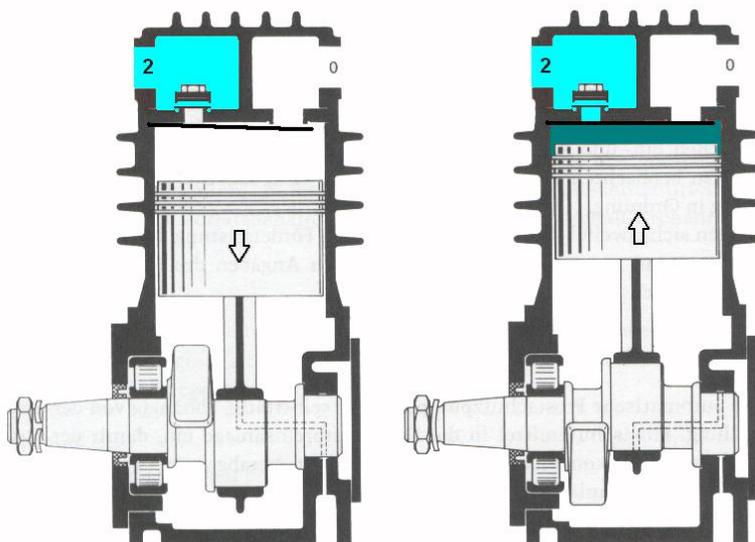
(слева): смазывание компрессора под давлением, обеспечиваемым системой смазки двигателя. Процесс впуска свежей порции воздуха.
